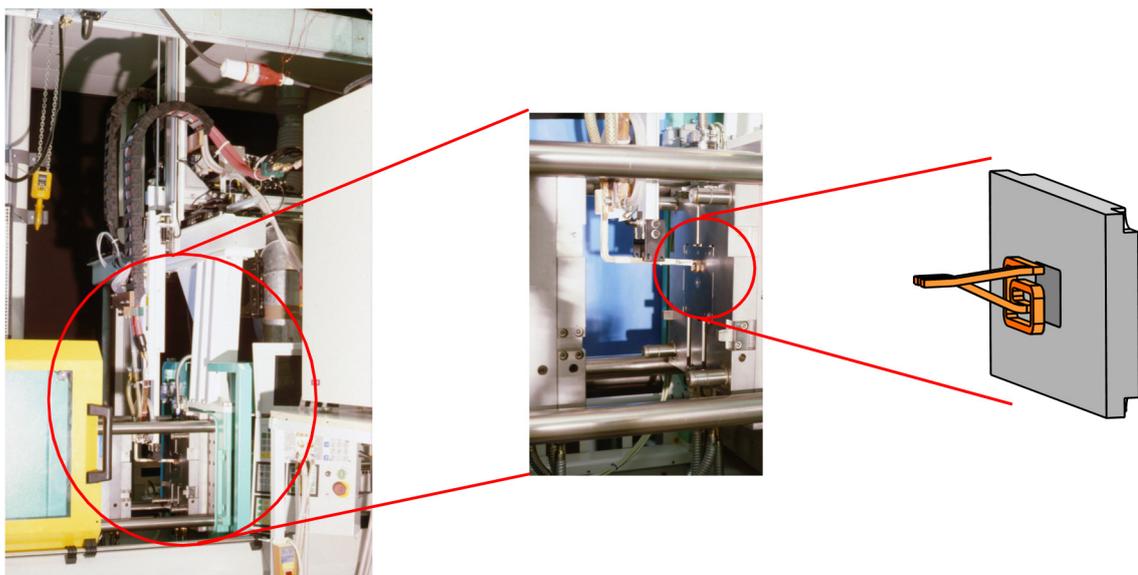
Gesamtanlage mit externem Induktor, links und Mitte Werkzeugbereich in der Spritzgießmaschine /22//127/
